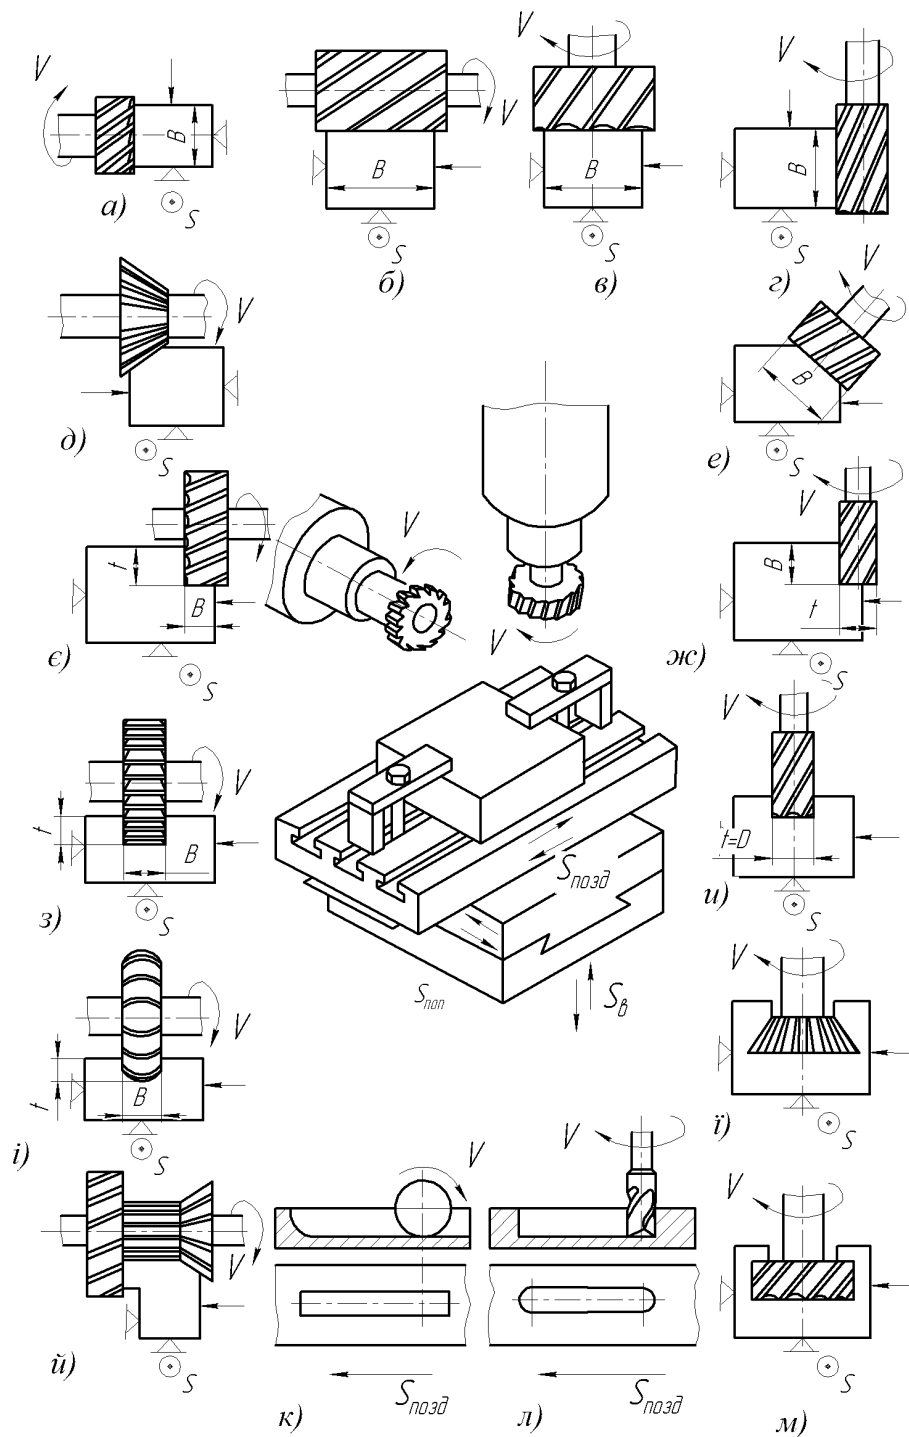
Схеми руху фрези і заготовки при фрезеруванні:
